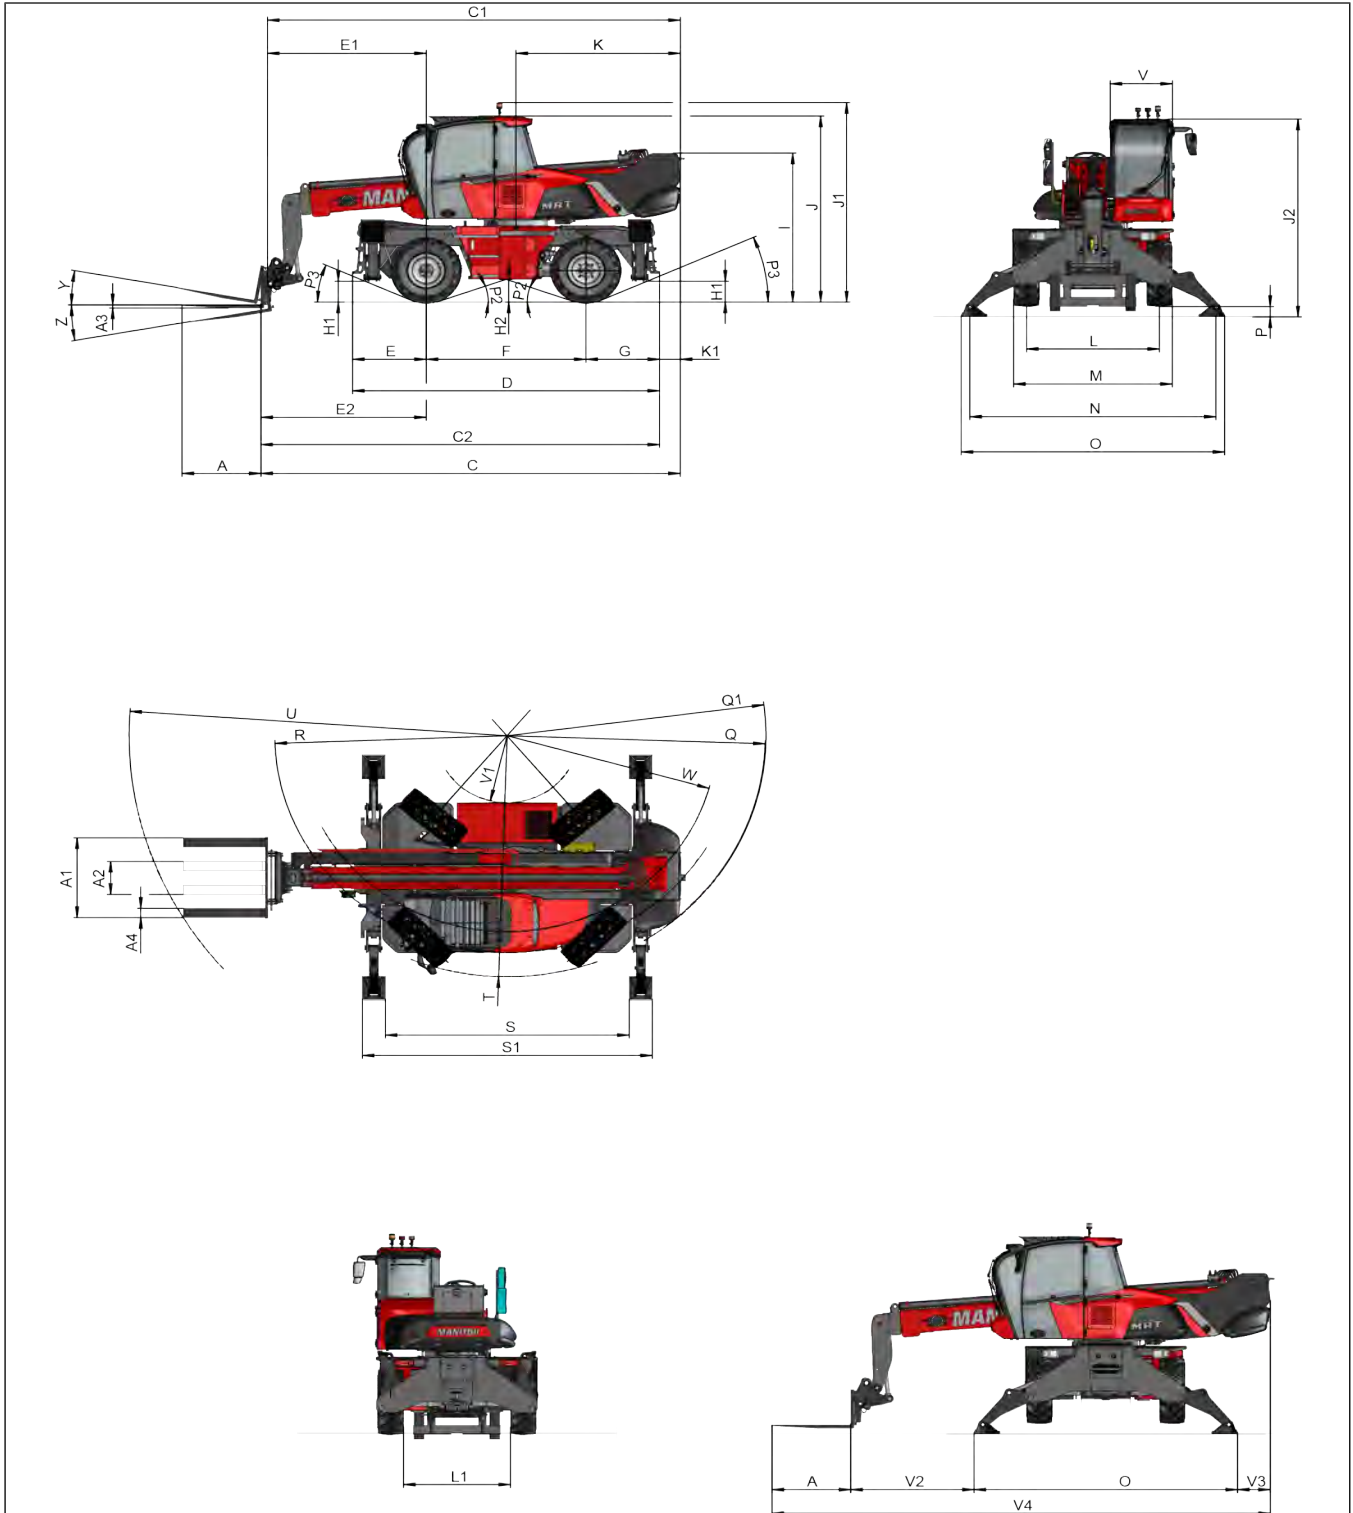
Dimensions (vue latérale, vue de face et vue de dessus)
